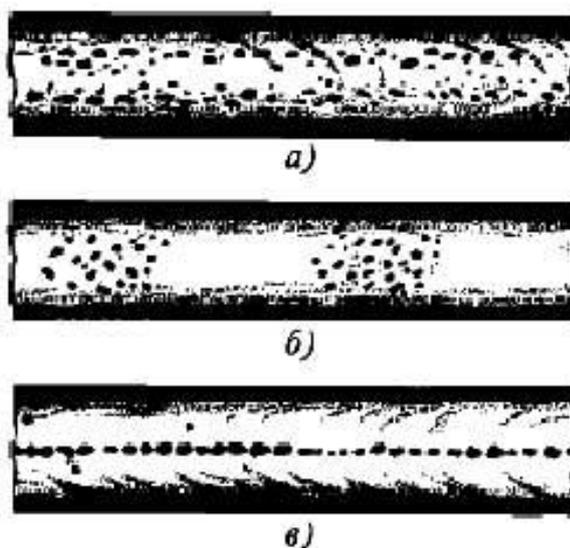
Поры (а), скопление пор (б) и цепочка пор (в) в сварном шве
